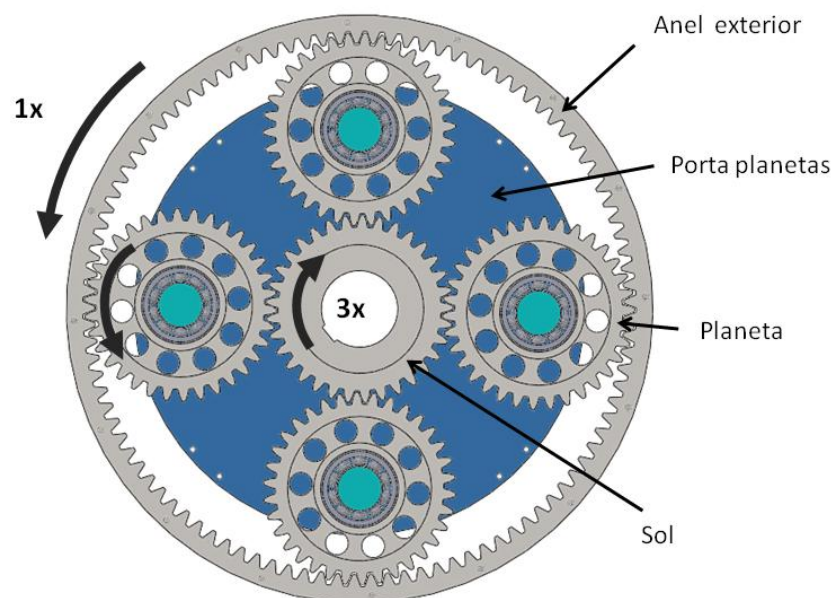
Engrenagem planetária com porta planetas visível.
